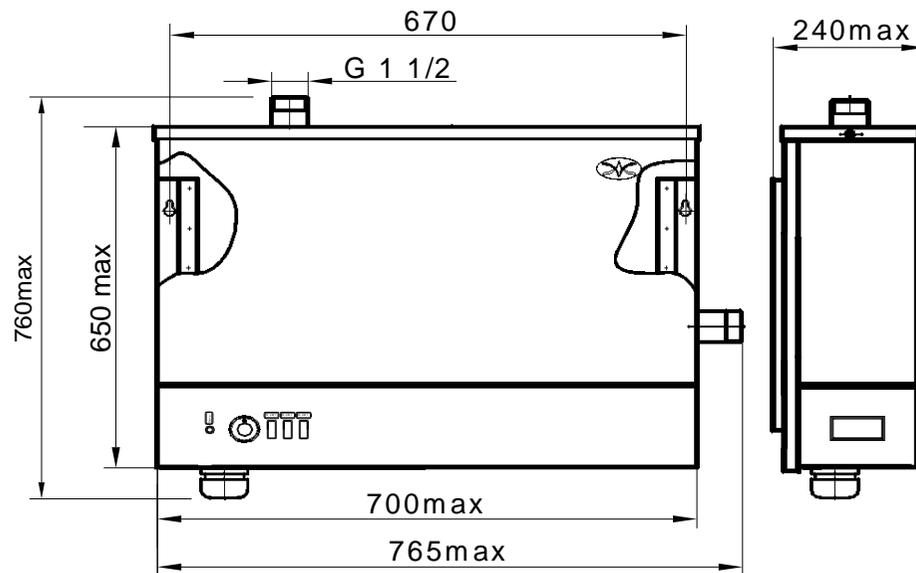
Водонагреватель ЭВПМ-72. Габаритный чертеж.
